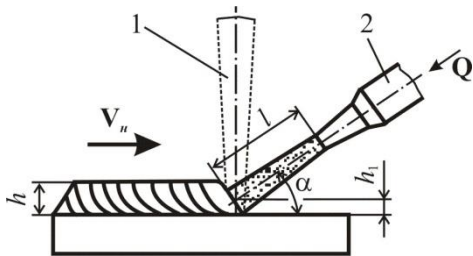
Схема процесса газопорошковой лазерной наплавки:
